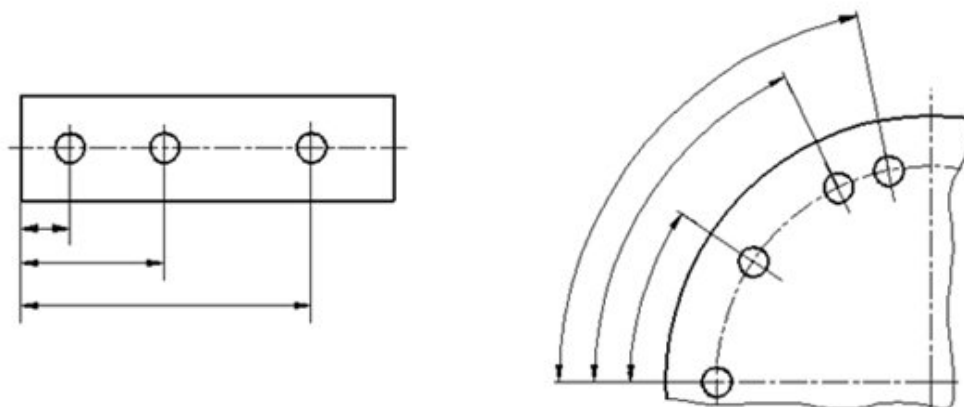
Нанесение размеров на деталях с равномерно расположенными одинаковыми элементами
